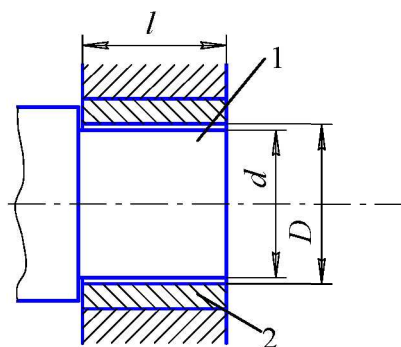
Основные размеры радиального подшипника скольжения: 1 – вал; 2 – вкладыш подшипника
